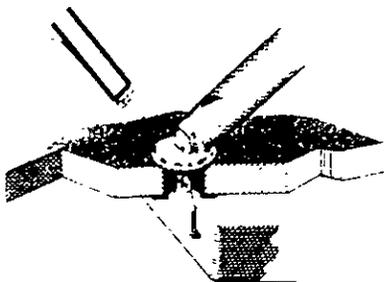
La soldadura se acumula solamente en una cara primero por lo tanto hay que mantener el caudín aplicado hasta que el baño cae, lo que indica que la soldadura ha corrido por el agujero
